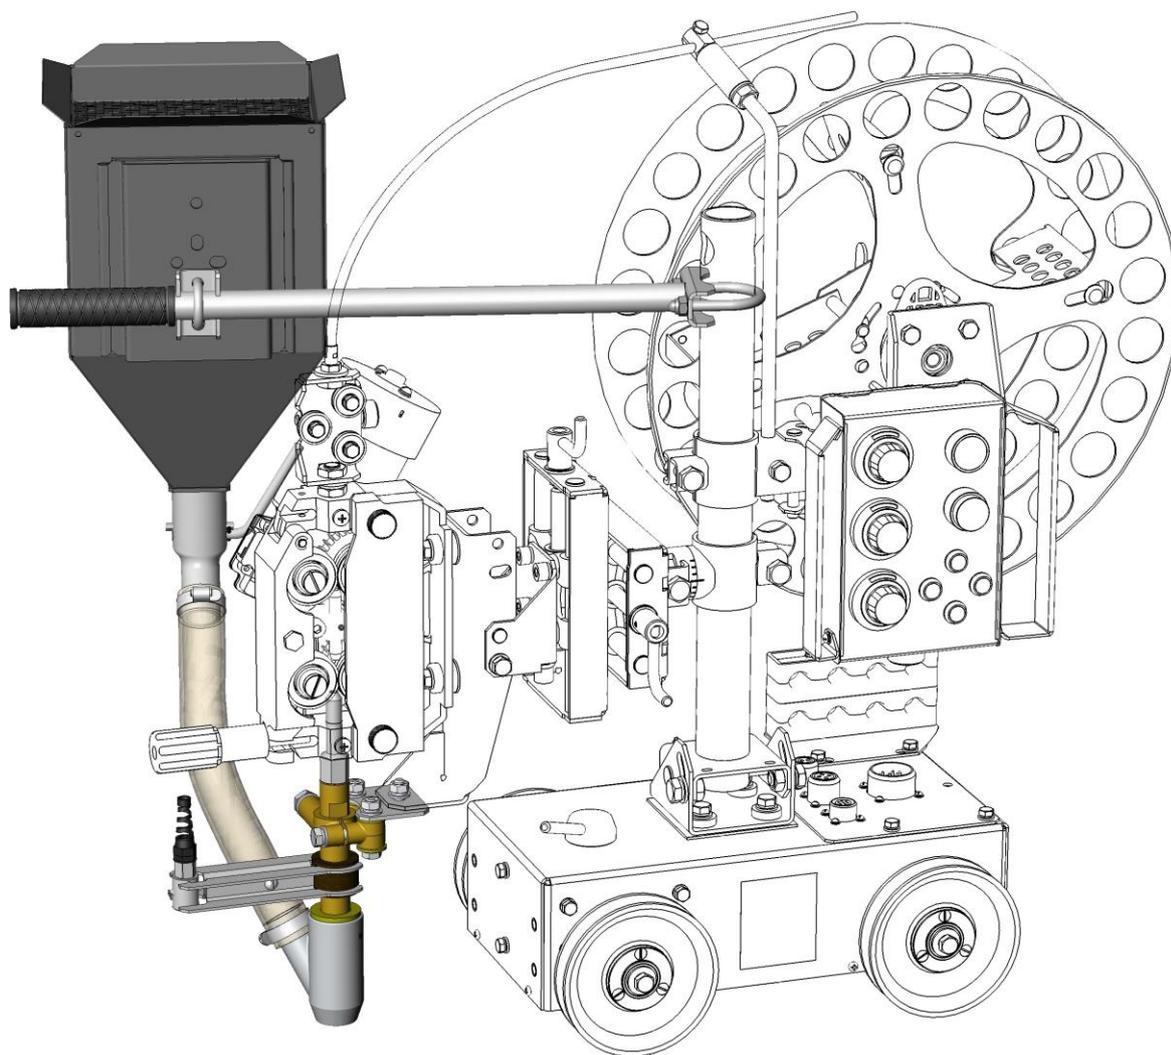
Комплект сварочной горелки для сварки под слоем флюса проволокой $\varnothing 1,2-3,2$ мм.
